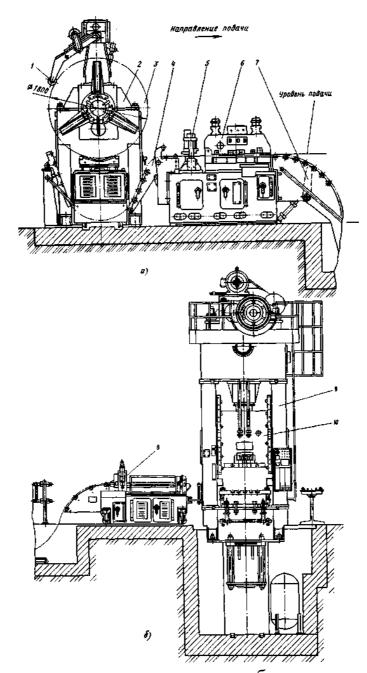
Типовая конструкция комплекса оборудования для штамповки деталей из рулонного материала (мод. АККА2036.01): a — разматывающие и правильные устройства;  $\delta$  — пресс с автоматической подачей
